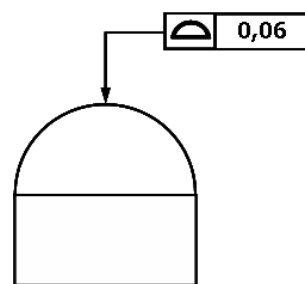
Indicação de tolerância de forma de uma superfície qualquer em desenho técnico
